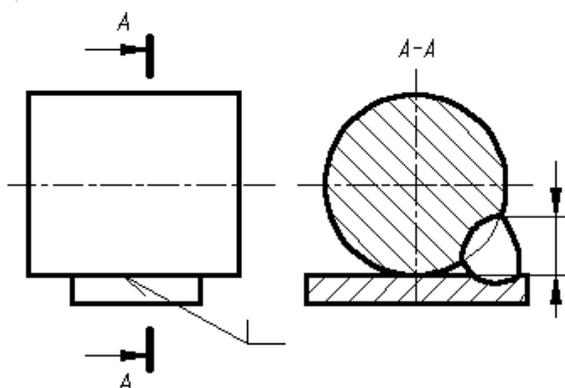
Шов соединения без скоса кромок, односторонний, выполненный ручной дуговой сваркой
